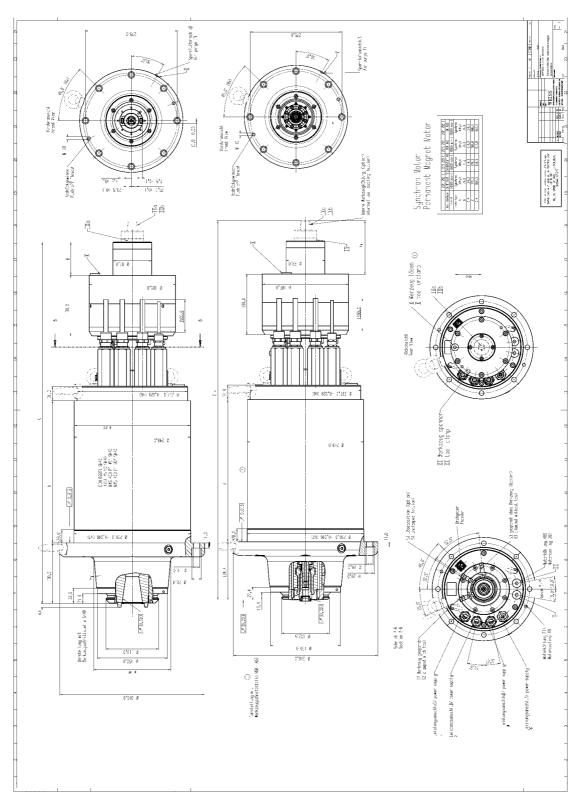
Disegno quotato mandrino 2SP125□-1□□0 (unità di sbloccaggio pneumatica)
